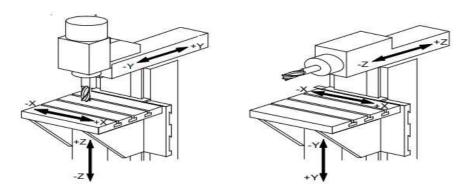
Система координат вертикально-фрезерного станка и горизонтальнофрезерного станка
